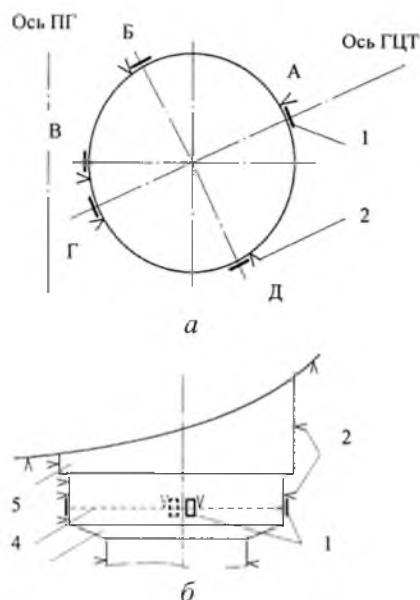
Схема установки датчиков при НТТМ узла приварки: *a* – вид сверху; *b* – вид сбоку. (1 – тензодатчик; 2 – термопара; 3 – коллектор парогенератора; 4 – сварной шов; 5 – патрубок парогенератора; здесь и на рис. 3: точки *A*, *B*, *V*, *Г*, *Д* соответствуют месту установки тензодатчиков.)
